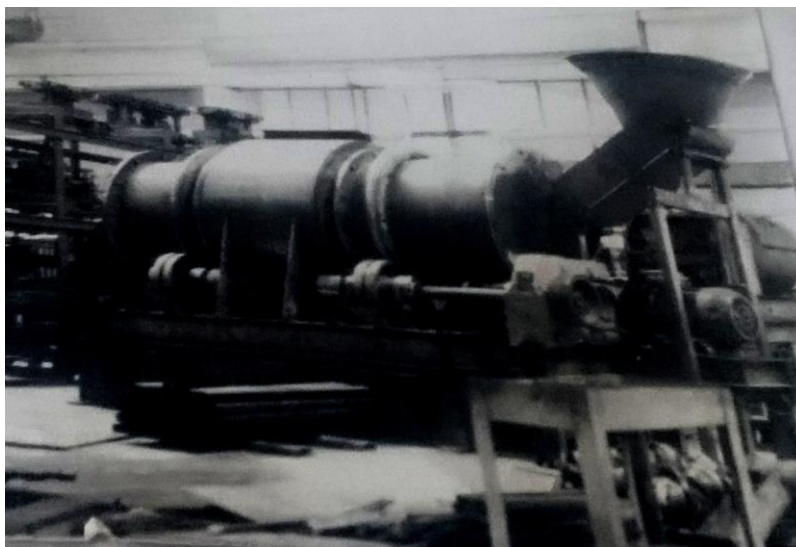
Станок непрерывного действия для ОЗУО на базе роторно-винтовой системы
